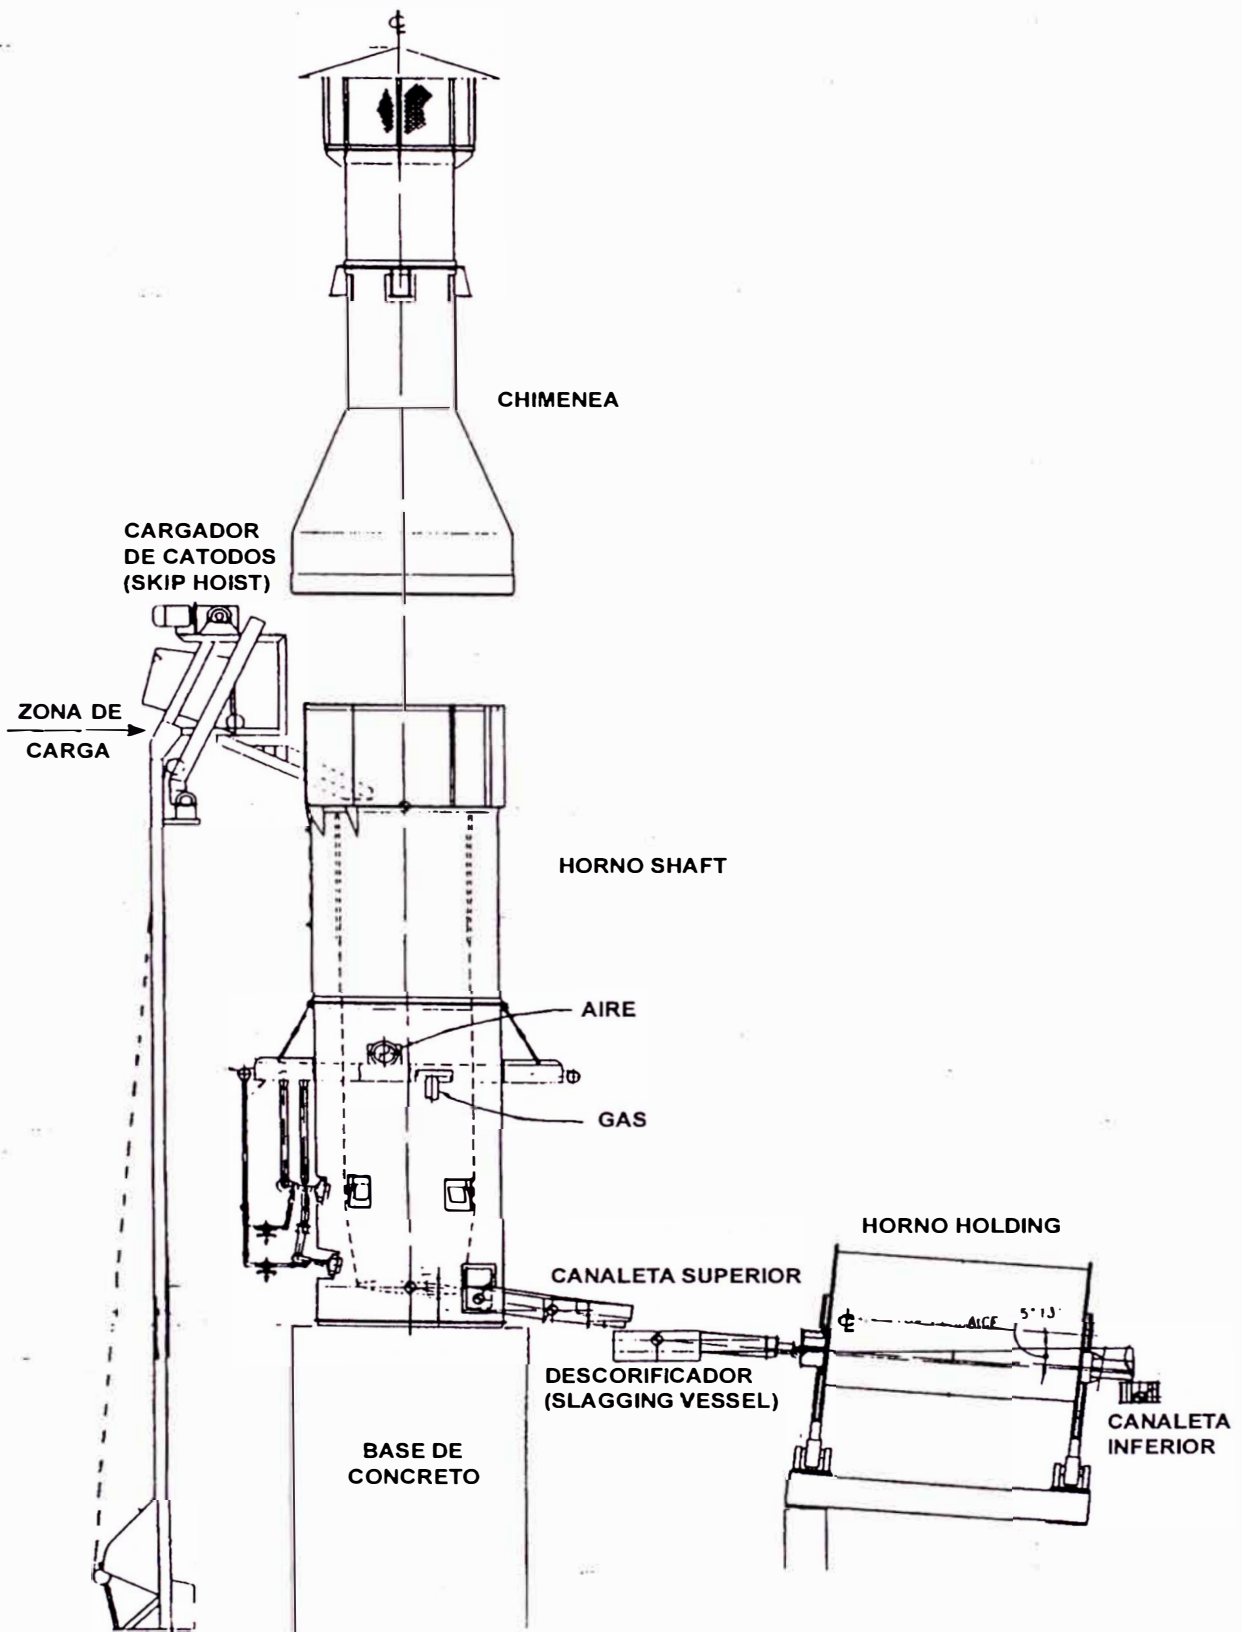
Hornos Shaft y Holding (vista frontal)
